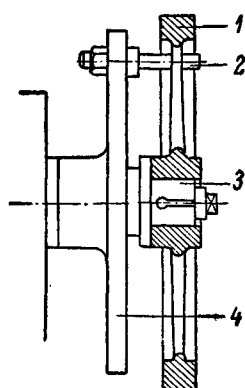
Оправки для закрепления деталей за резьбовое отверстие
